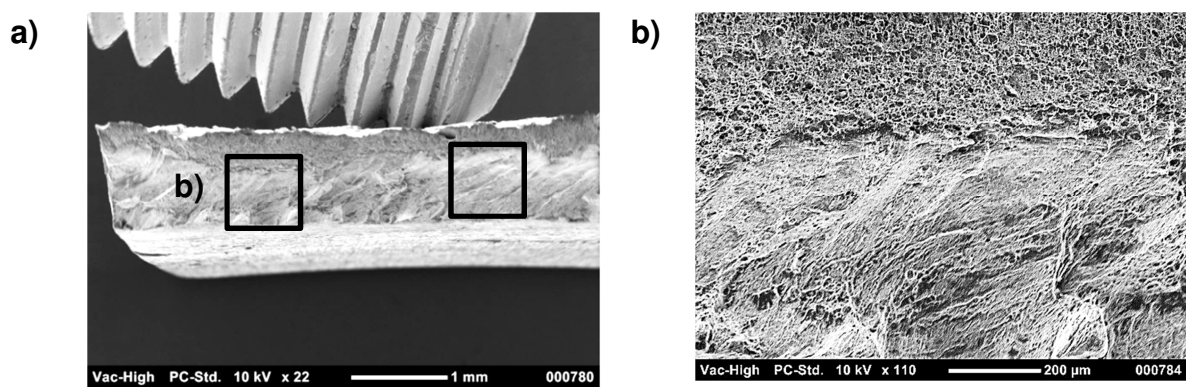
Fraktographische Detailaufnahmen der FSW-Verbindung ISF-33-00032
